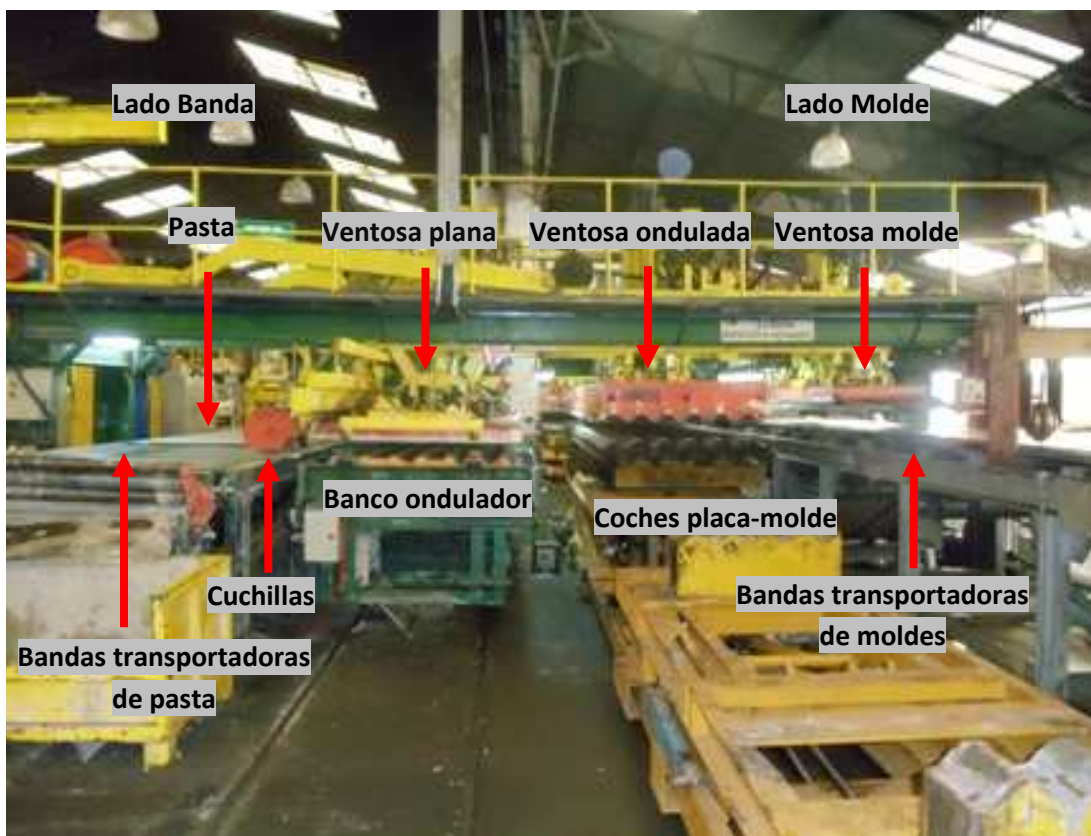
Pórtico 2 vista posterior, ventosas arriba, sobre el lado molde
